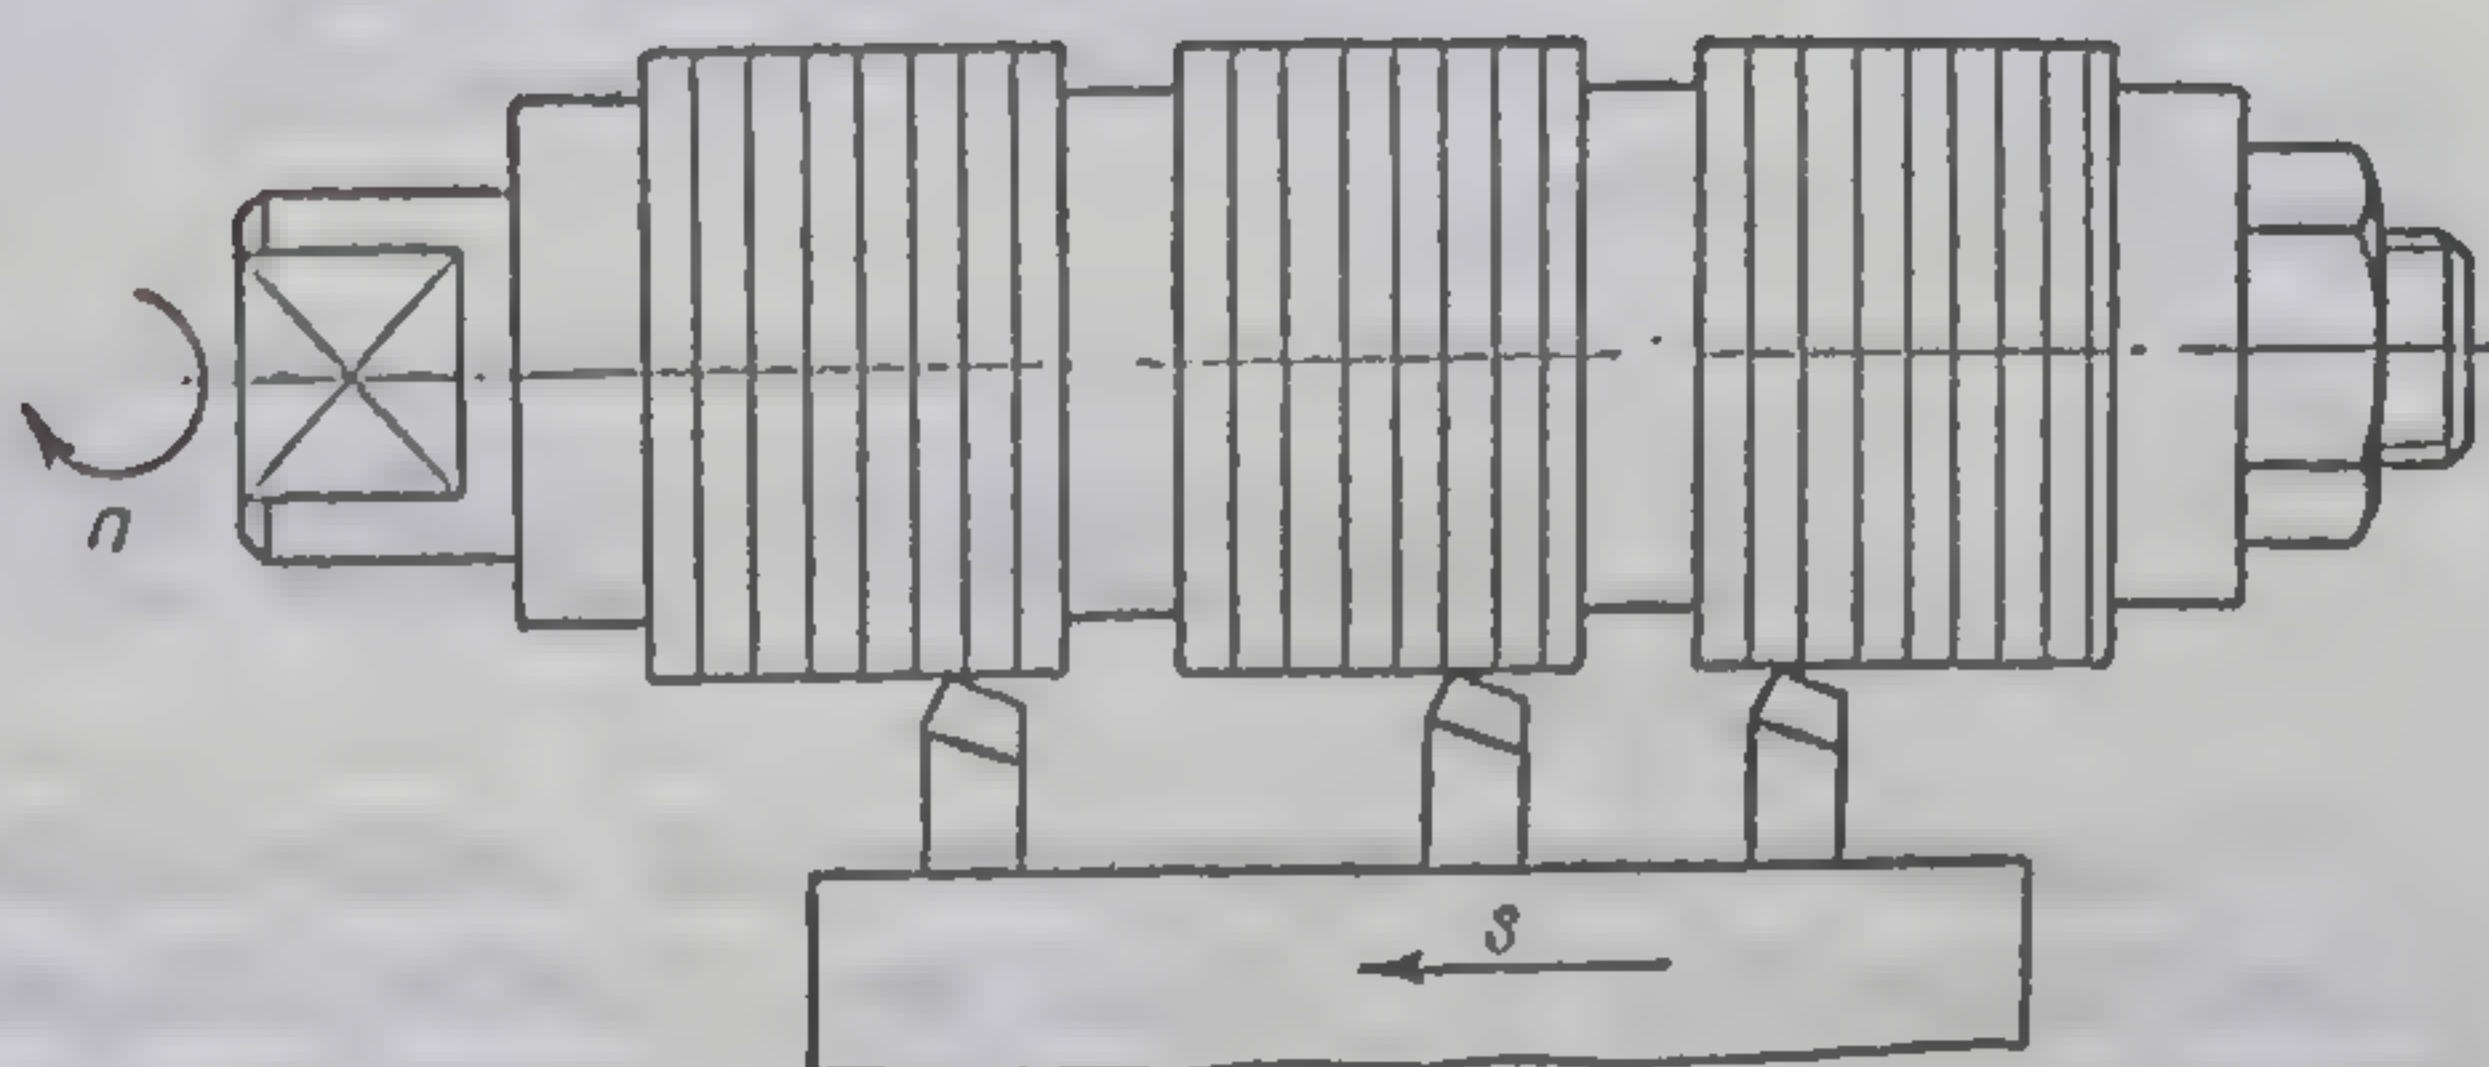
Dispozitiv pentru strunjirea exterioară a segmentelor.
